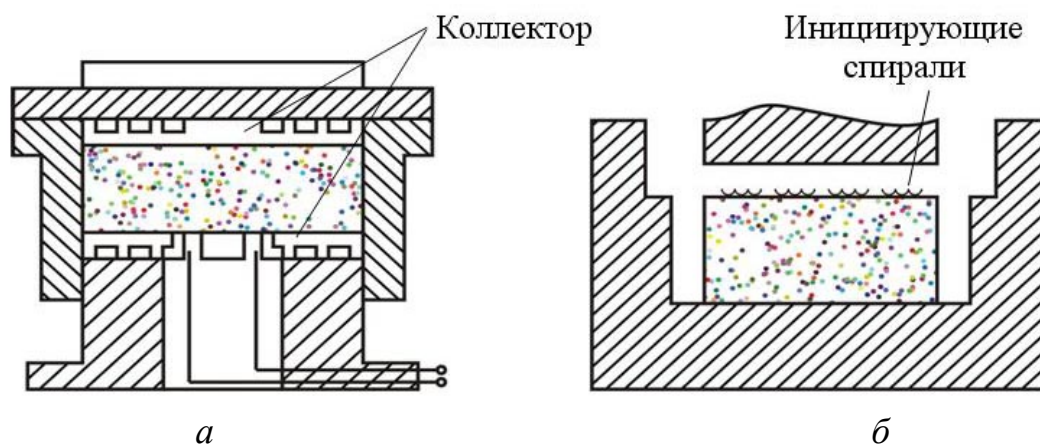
Схемы реакционных пресс-форм для крупногабаритных заготовок:
